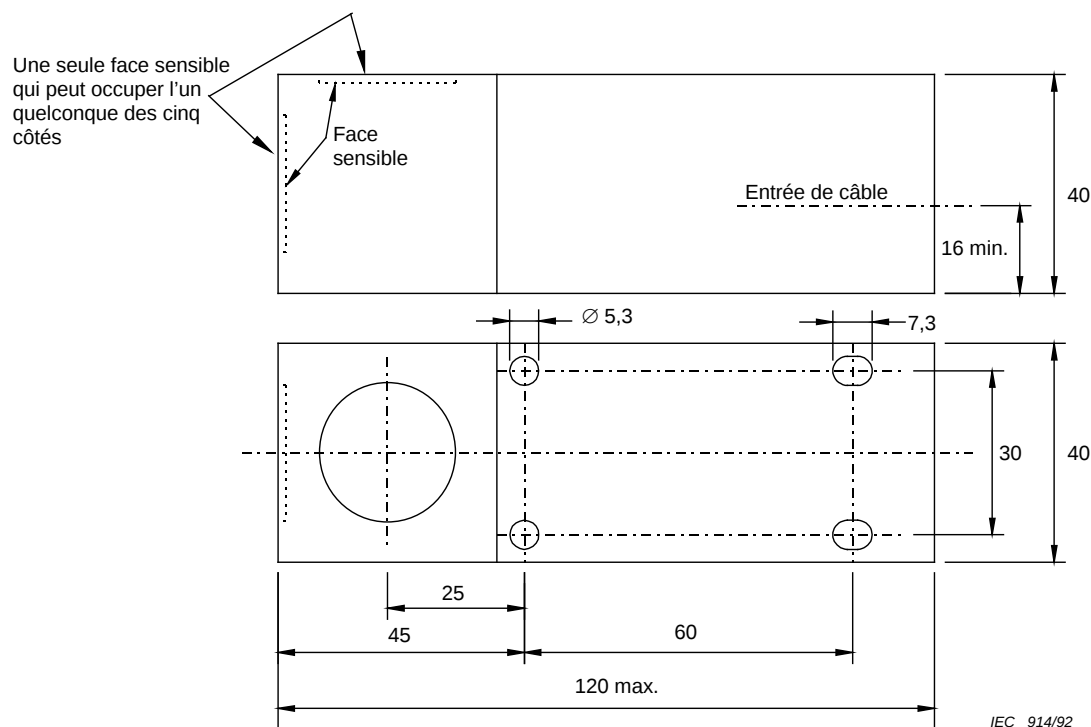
(CC) b – Dimensions, type C40 en millimètres
